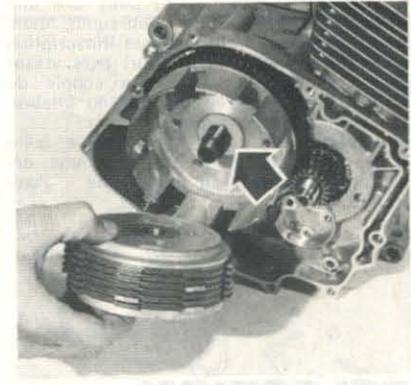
Rondelle crénelée au fond de la cloche (Photo RMT)
